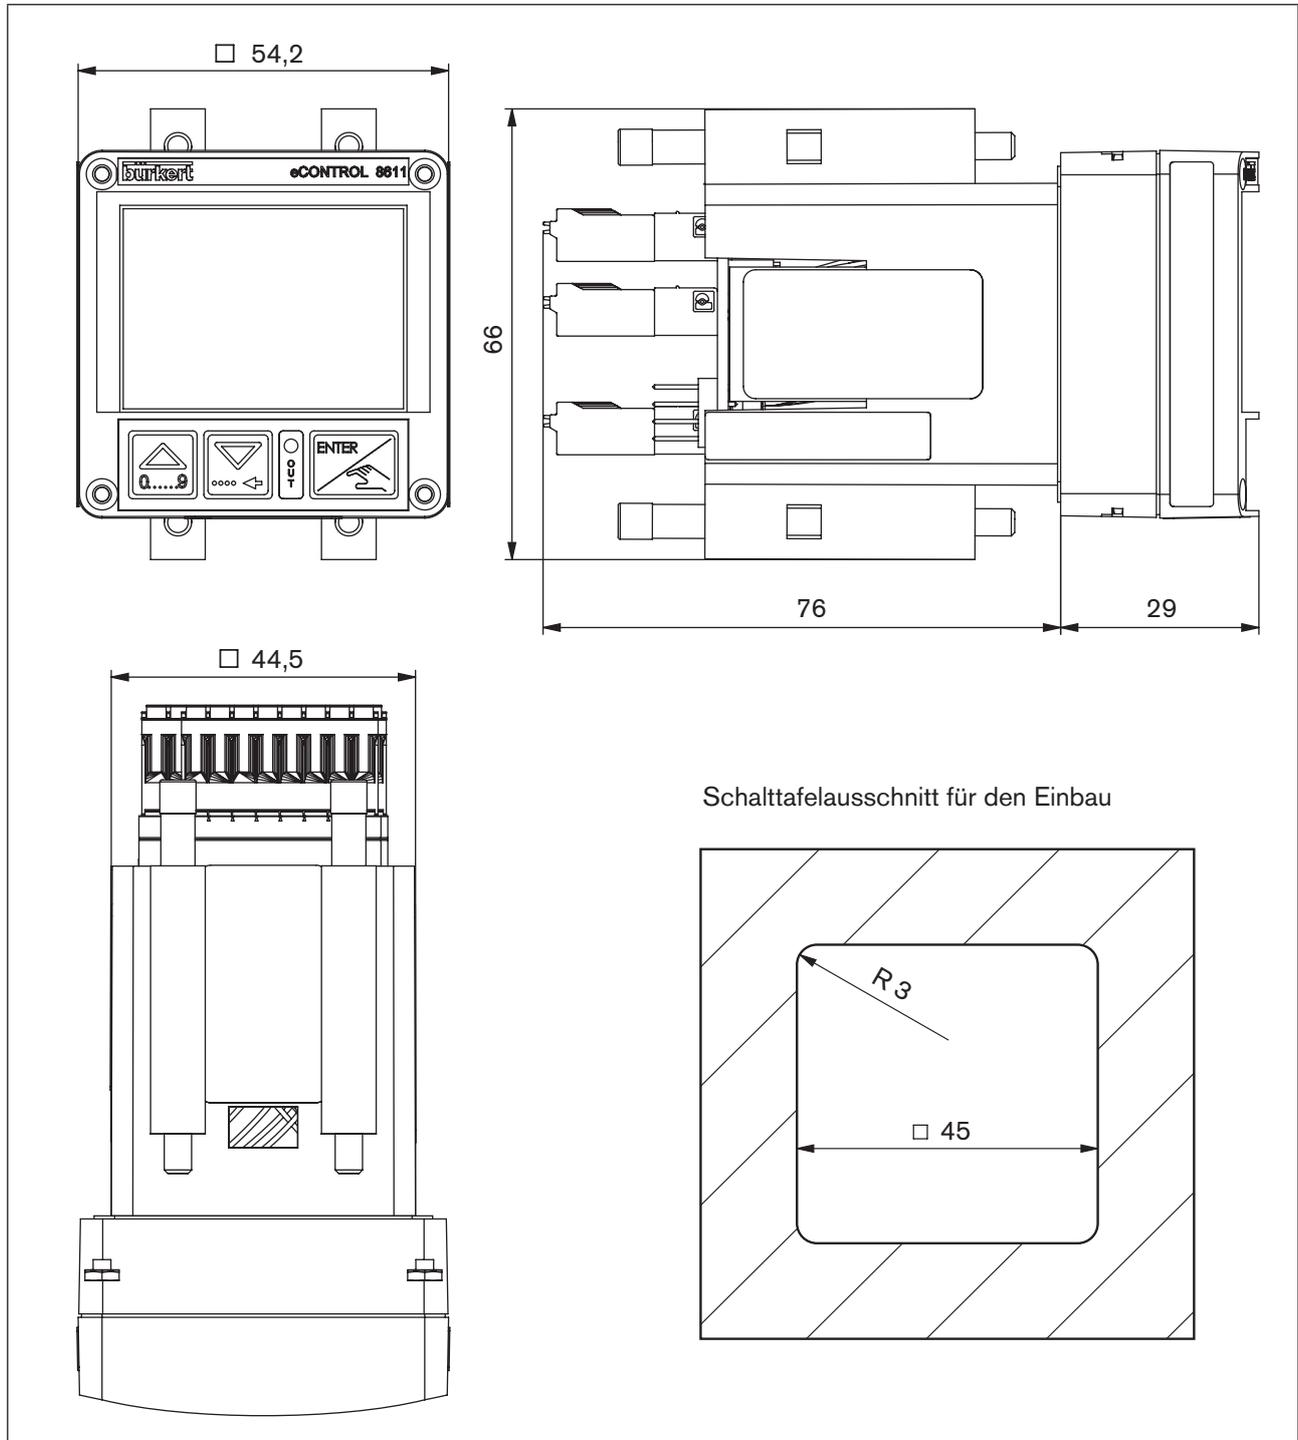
Geräteabmessungen und Schalttafelausschnitt
